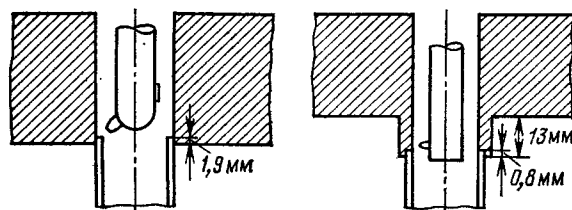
Сварка концов труб изнутри (размеры для трубы с наружным диаметром 19 мм)
